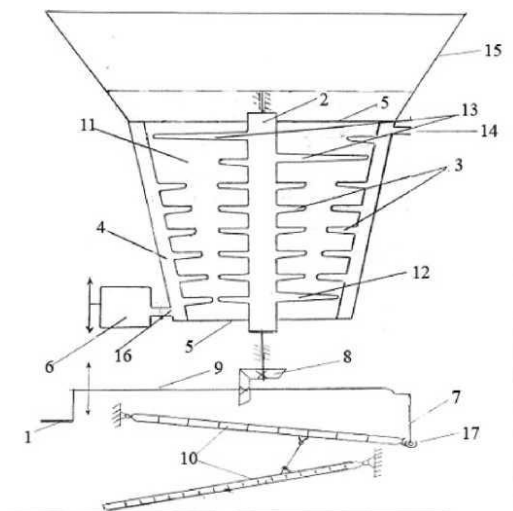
Принципова схема шишко-подрібнювача Попова А.Т.:
